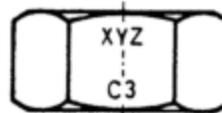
Beispiele für die Kennzeichnung von Schrauben
